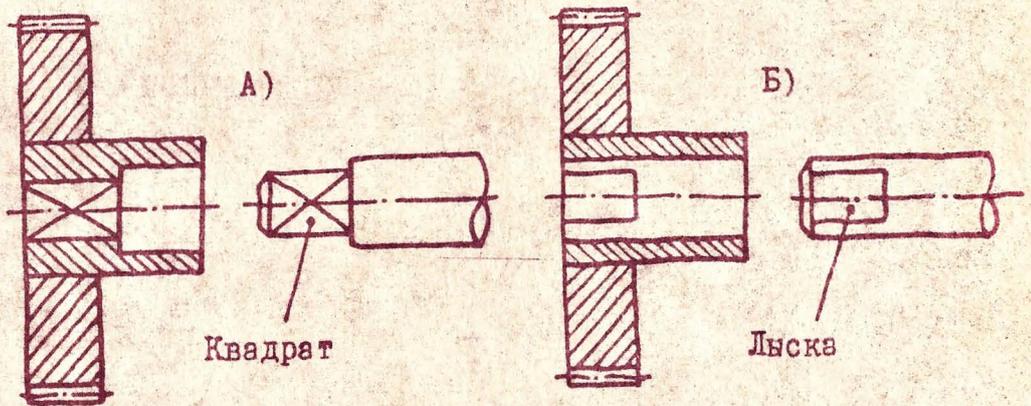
Соединение выходного колеса редуктора с хвостовиком вала шнека
